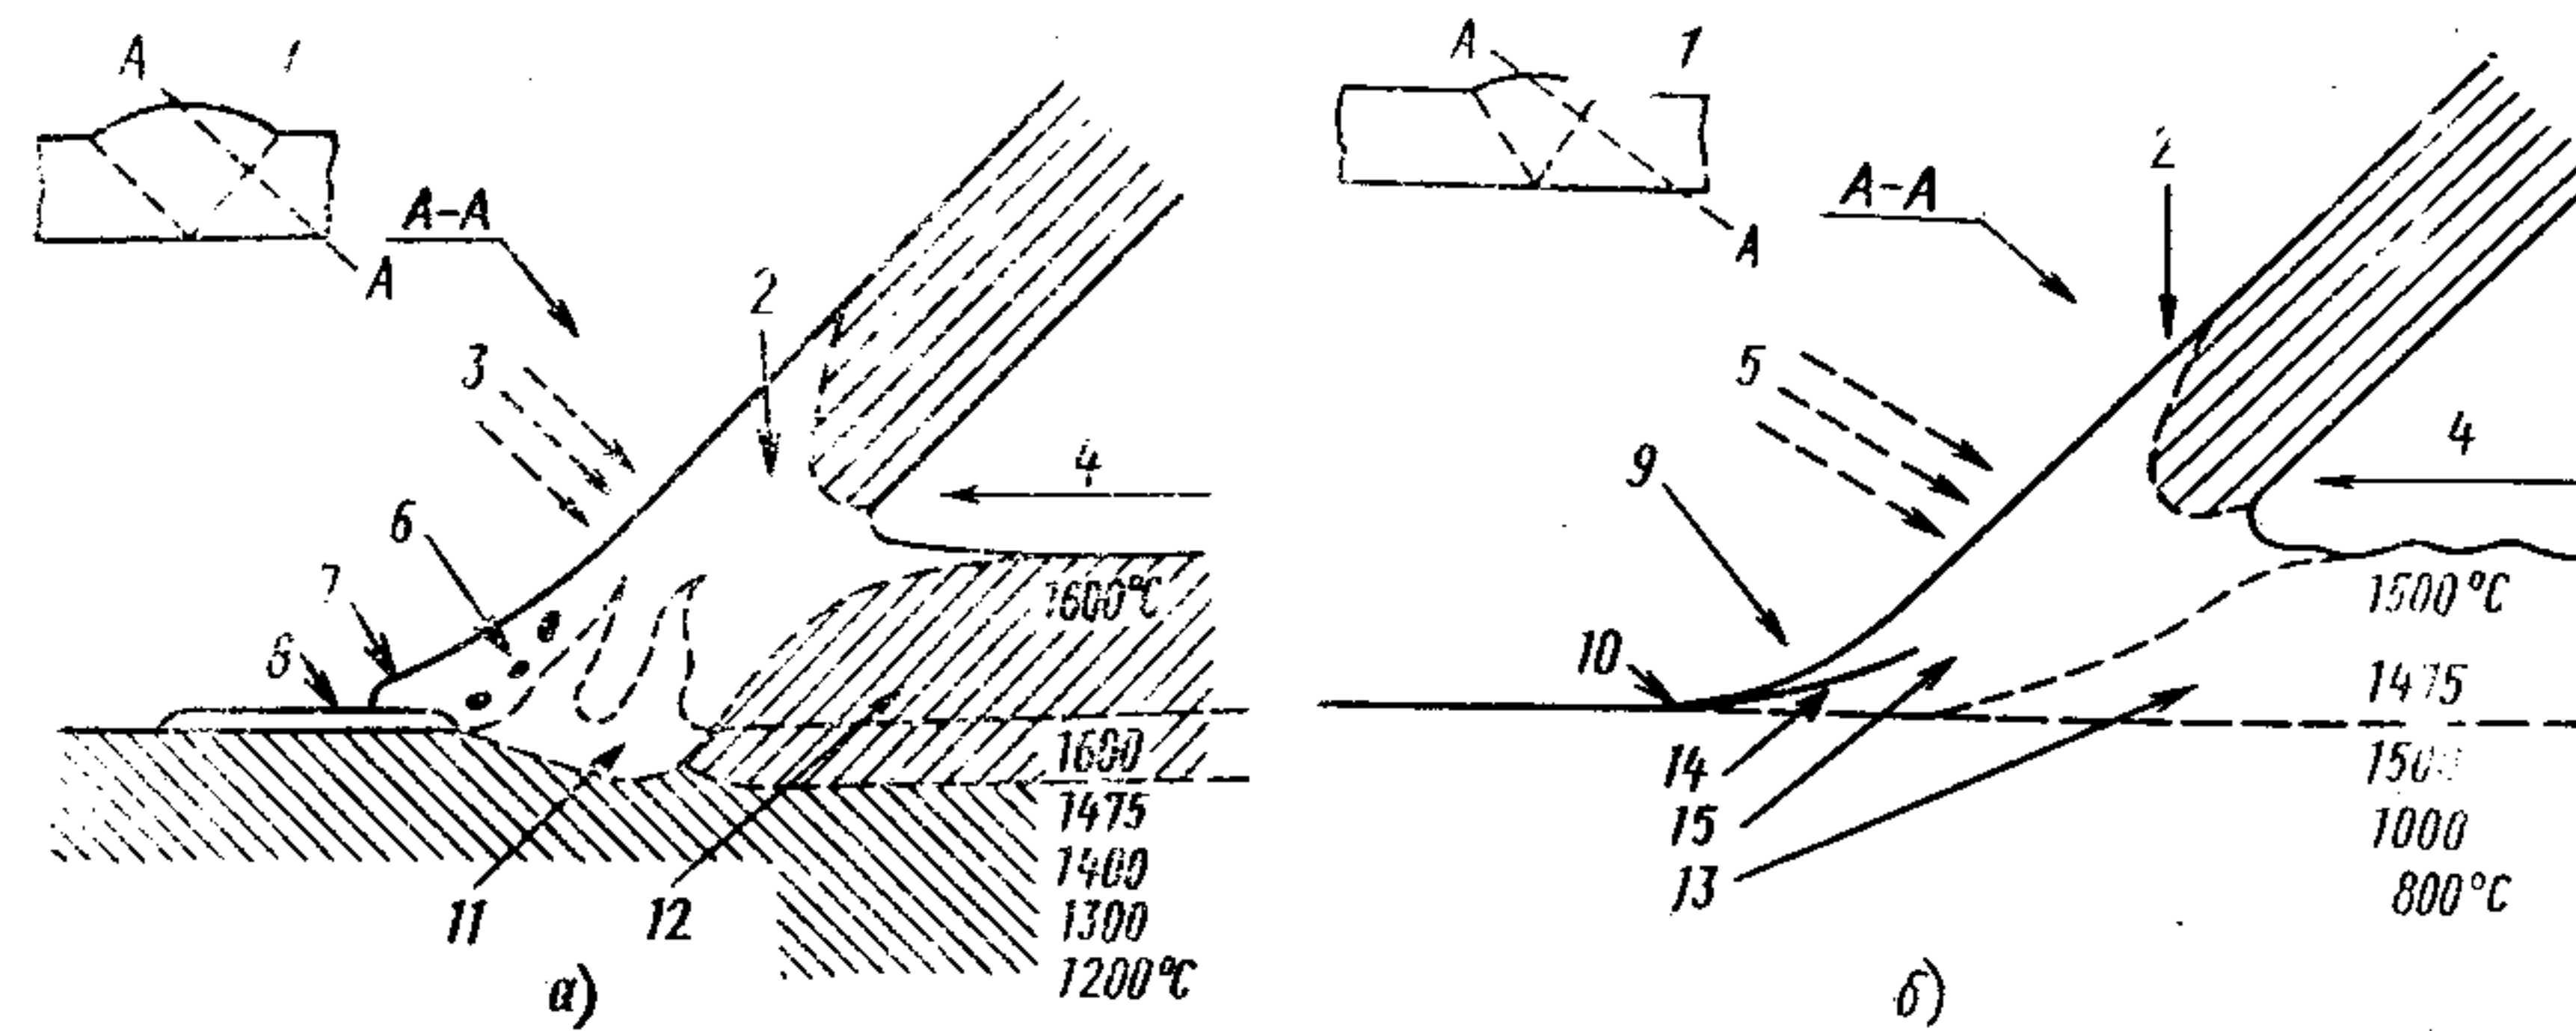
Схема дуговой сварки (наплавки) стали:
